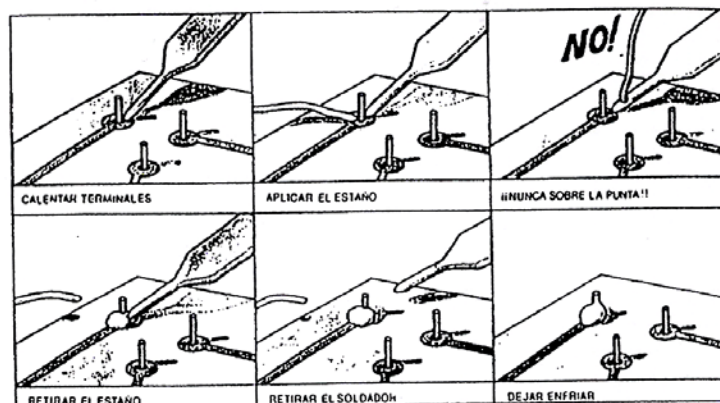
Algunes indicacions per aconseguir una soldadura correcta.
